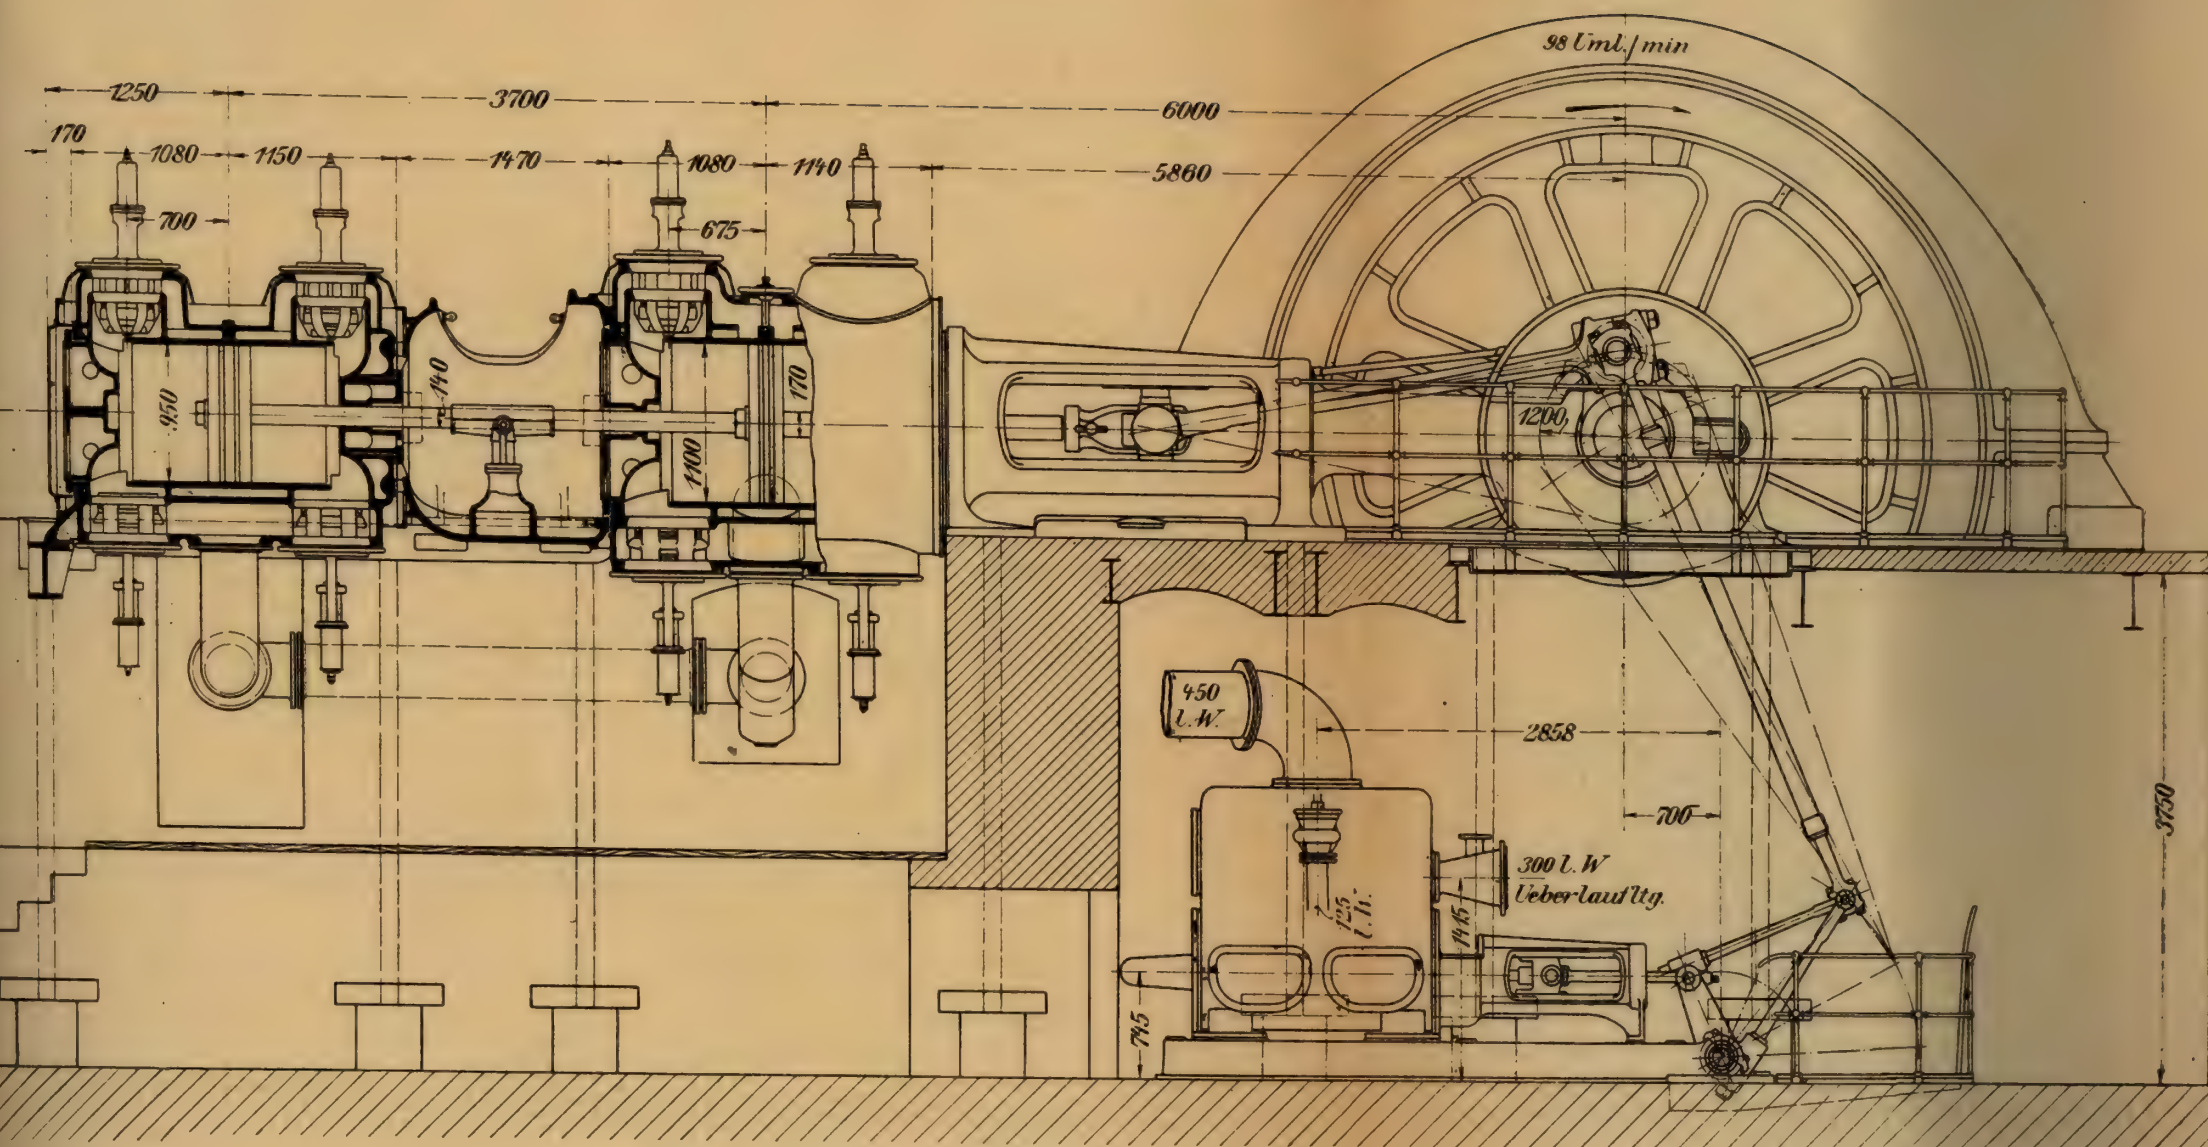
Aufriß und Schnitt durch die Zylinder.
